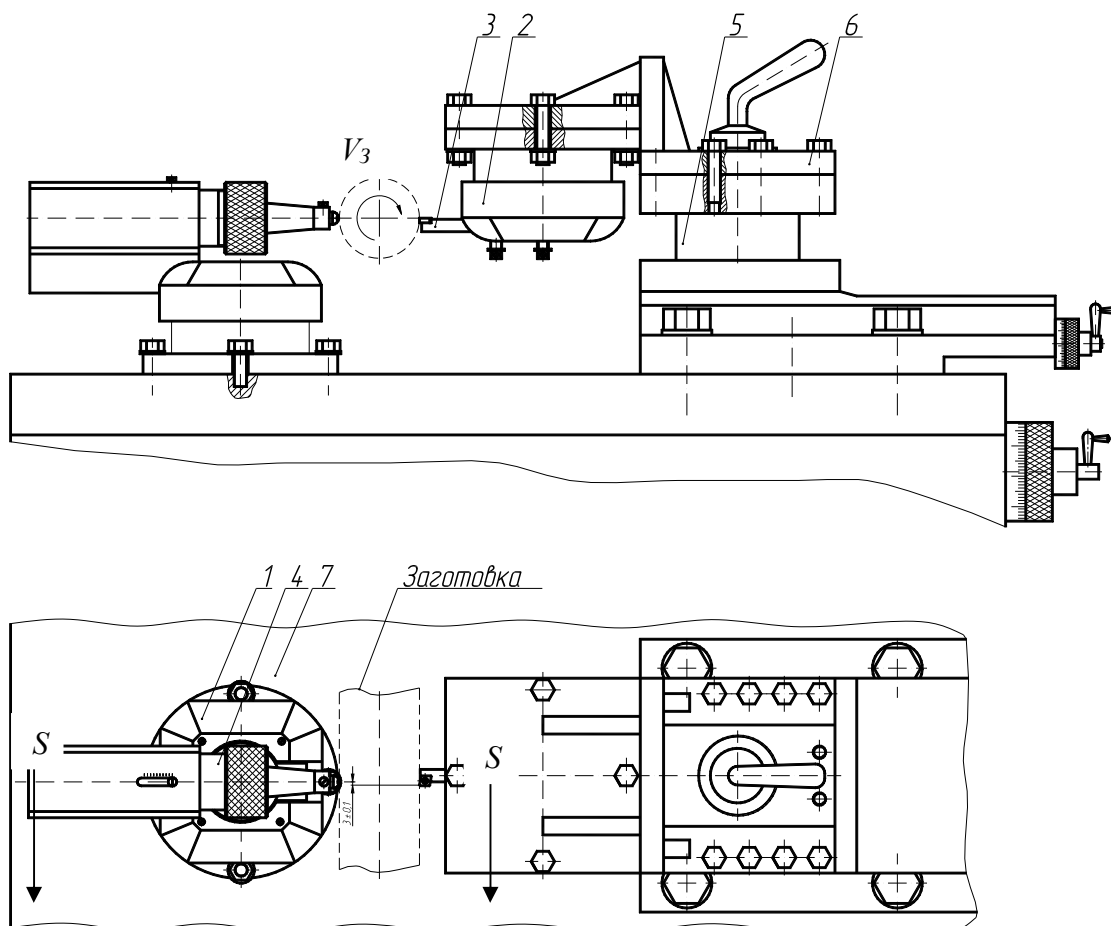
Устройство для комбинированной обработки точением и ультразвуковым твердосплавным выглаживанием: 1, 2 – динамометр УДМ-100; 3 – резец, оснащенный сменной многогранной пластиной из твёрдого сплава; 4 – устройство для УЗТВ заготовок; 5 – резцедержатель; 6 – кронштейн; 7 – суппорт станка
